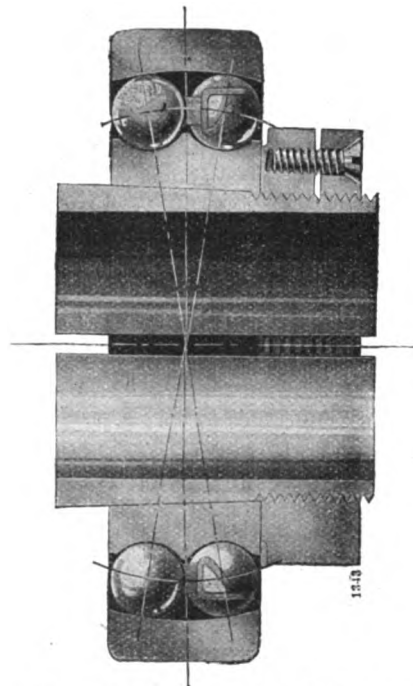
Coupe d'un roulement SKF à rotule sur billes, avec manchon de serrage permettant la fixation sur l'arbre.
